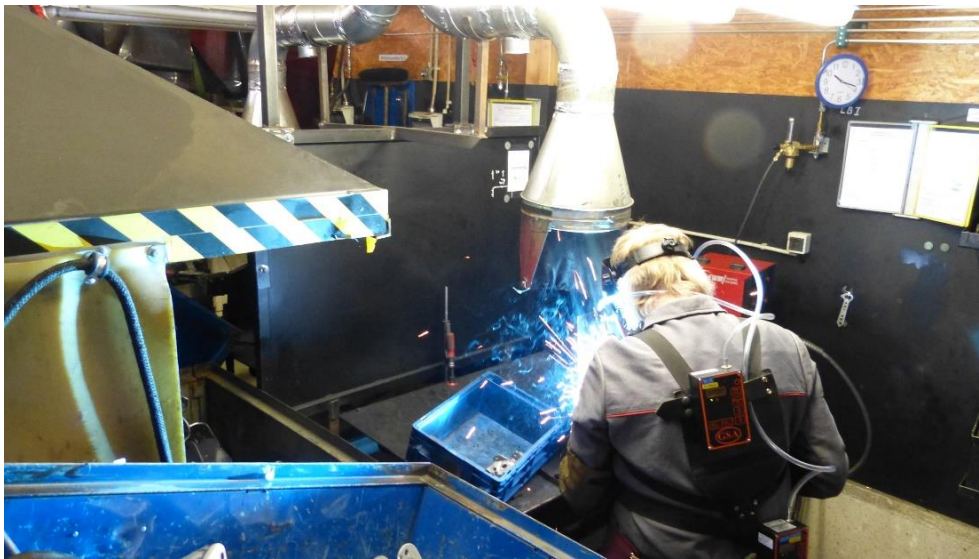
MAG-Schweißarbeitsplatz mit gut positionierter Absaugung
